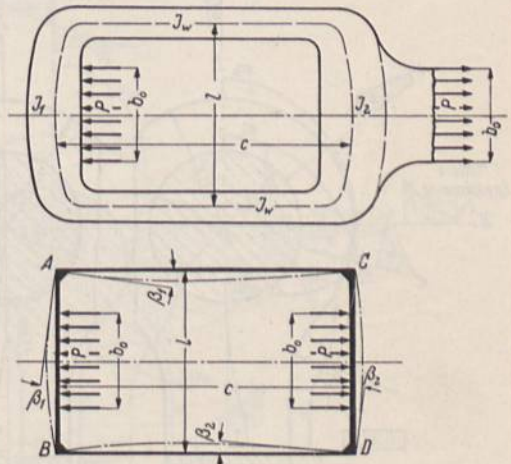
und 1246. Zur Berechnung geschlossener Schubstangenköpfe rechteckiger Grundform.
